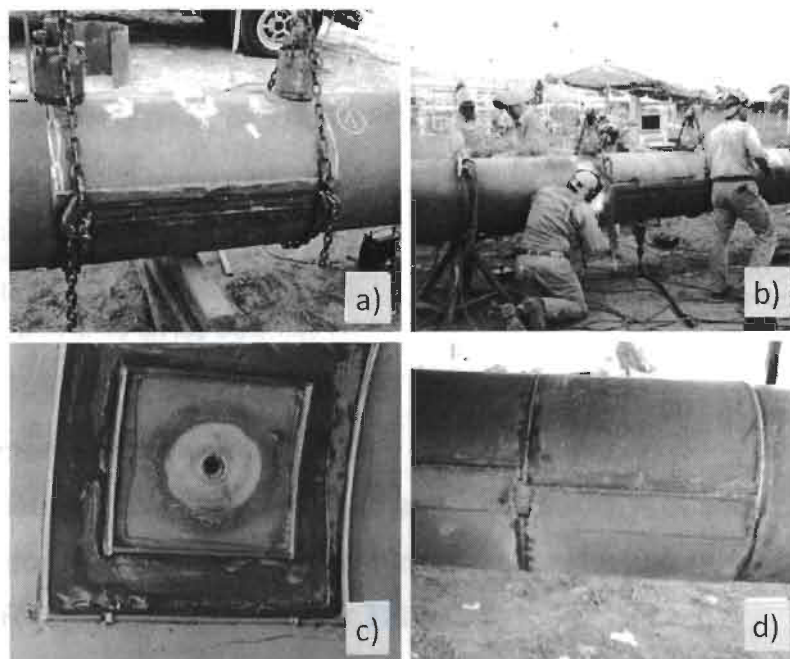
Etapas del proceso de encamisado. a) Método de fijación. b) soldadura en un tubo con fuga. c) Doble O'ring utilizado para contener la fuga. d) reforzamiento en tandem, con penetración total en la soldadura circular intermedia [16]
